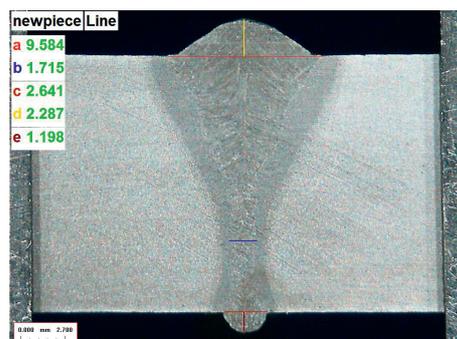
Макрошлиф таврового сварного шва, выполненный гибридной лазерной сваркой на скорости сварки 1,0 м/мин на пластинах толщиной 12 мм
